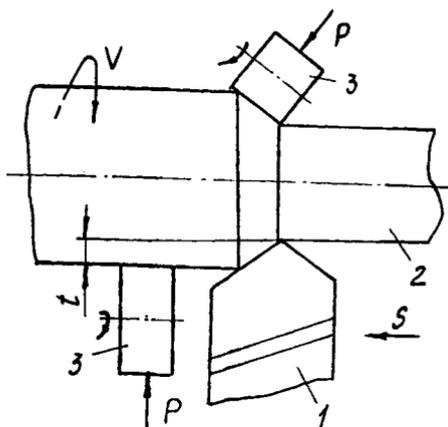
Схема обработки резанием с опережающим пластическим деформированием: 1 – резец; 2 – обрабатываемая заготовка; 3 – ролик
